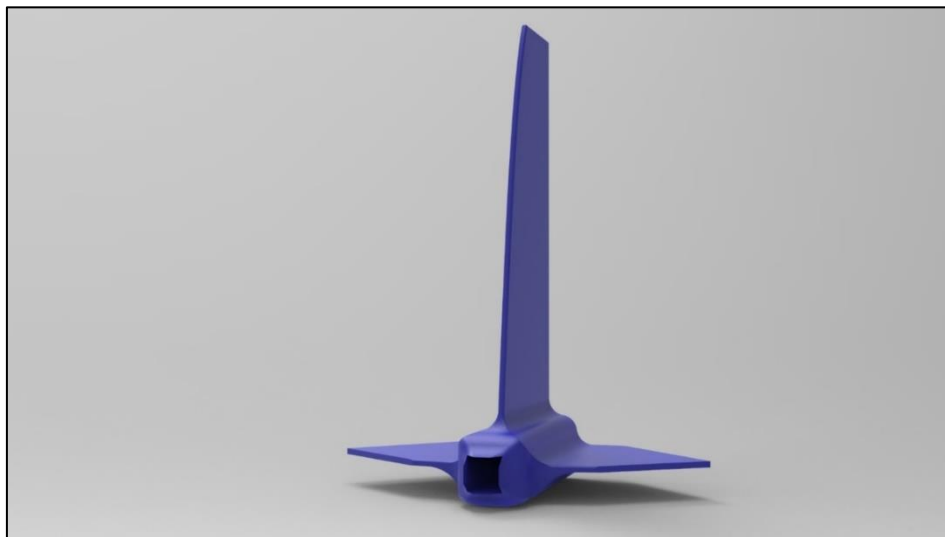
Sección central empenaje - vista isométrica [Autores].
